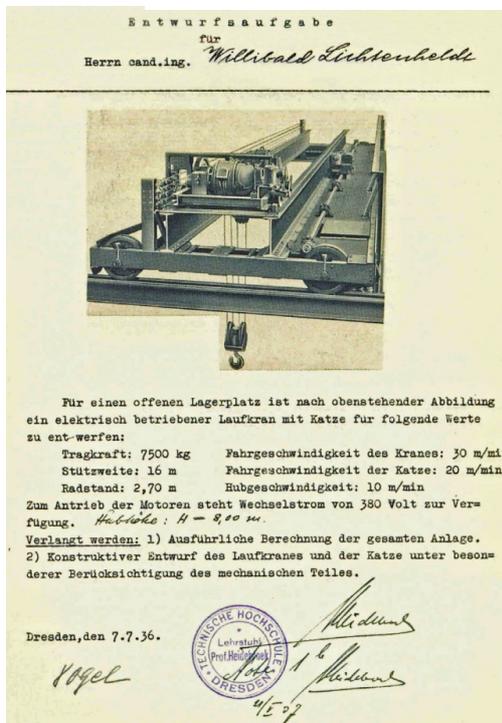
Diplomaufgabe für Willibald Lichtenheld Mauersberger, Maschinenbau an der TU Dresden
